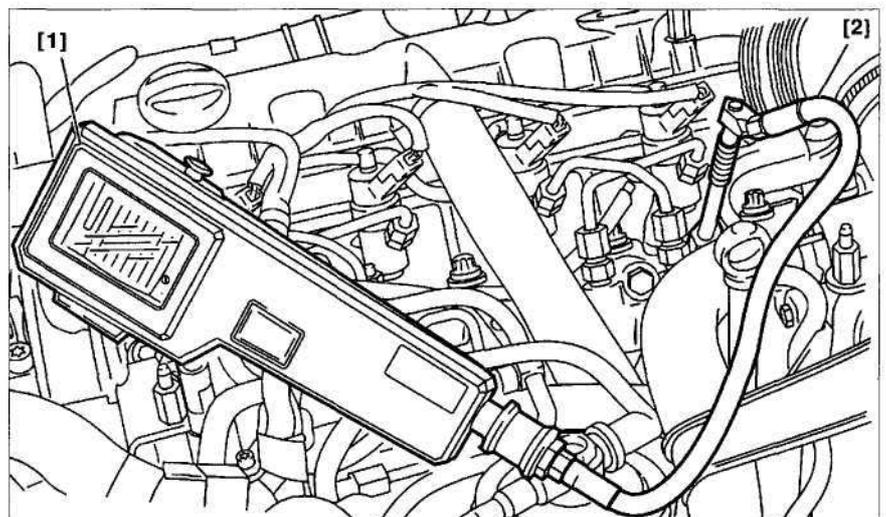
Вкрутите приспособление [2] в отверстие под свечу накаливания цилиндра №1. Присоедините тестер [1] к приспособлению [2].
